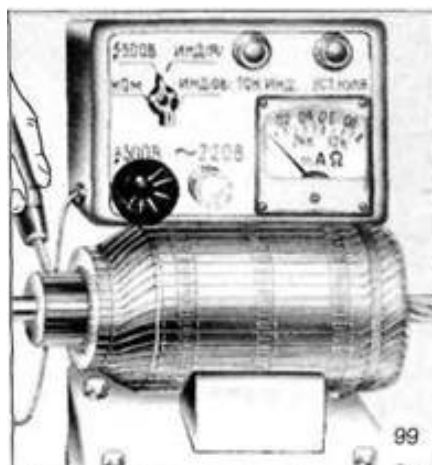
Перевірка обмотки якоря на замикання з корпусом
